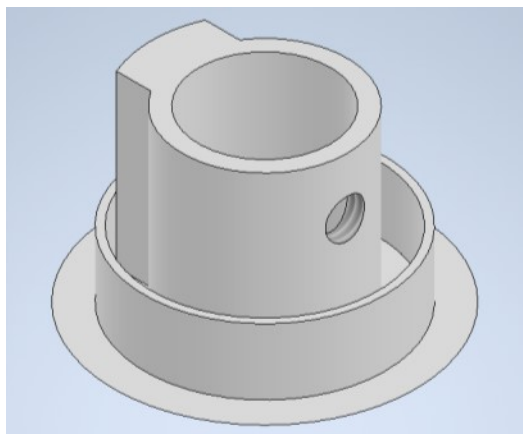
Finální provedení objímky s drážkou vytvořenou frézováním
